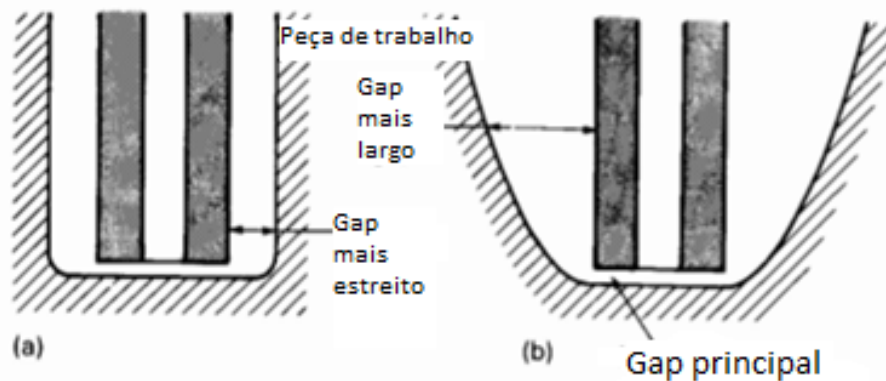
Desenho esquemático usinagem eletroquímica
